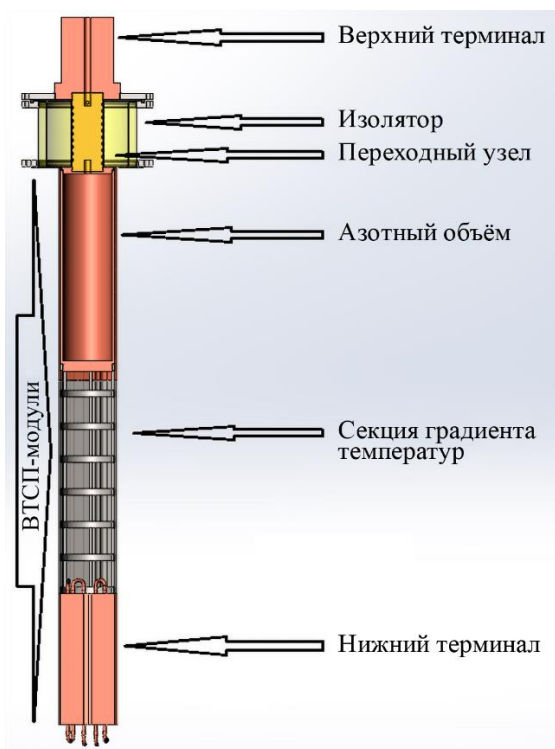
Общая схема конструкции разрабатываемого токоввода
